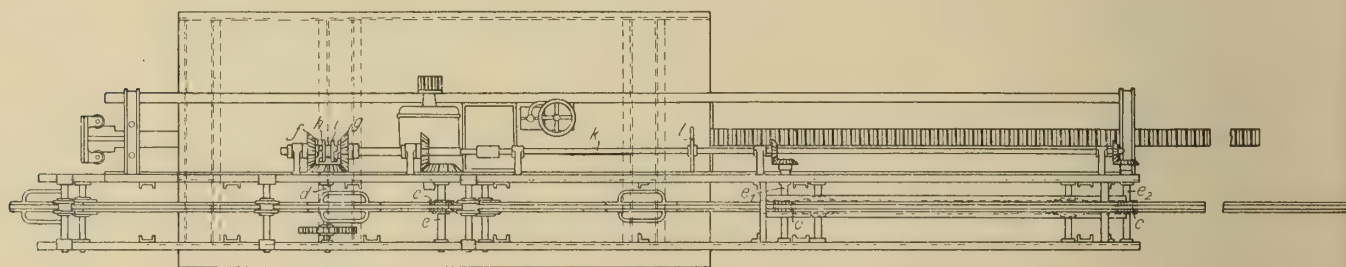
Oberansicht des Planierstangengetriebes der Schalker Eisenhütte.
